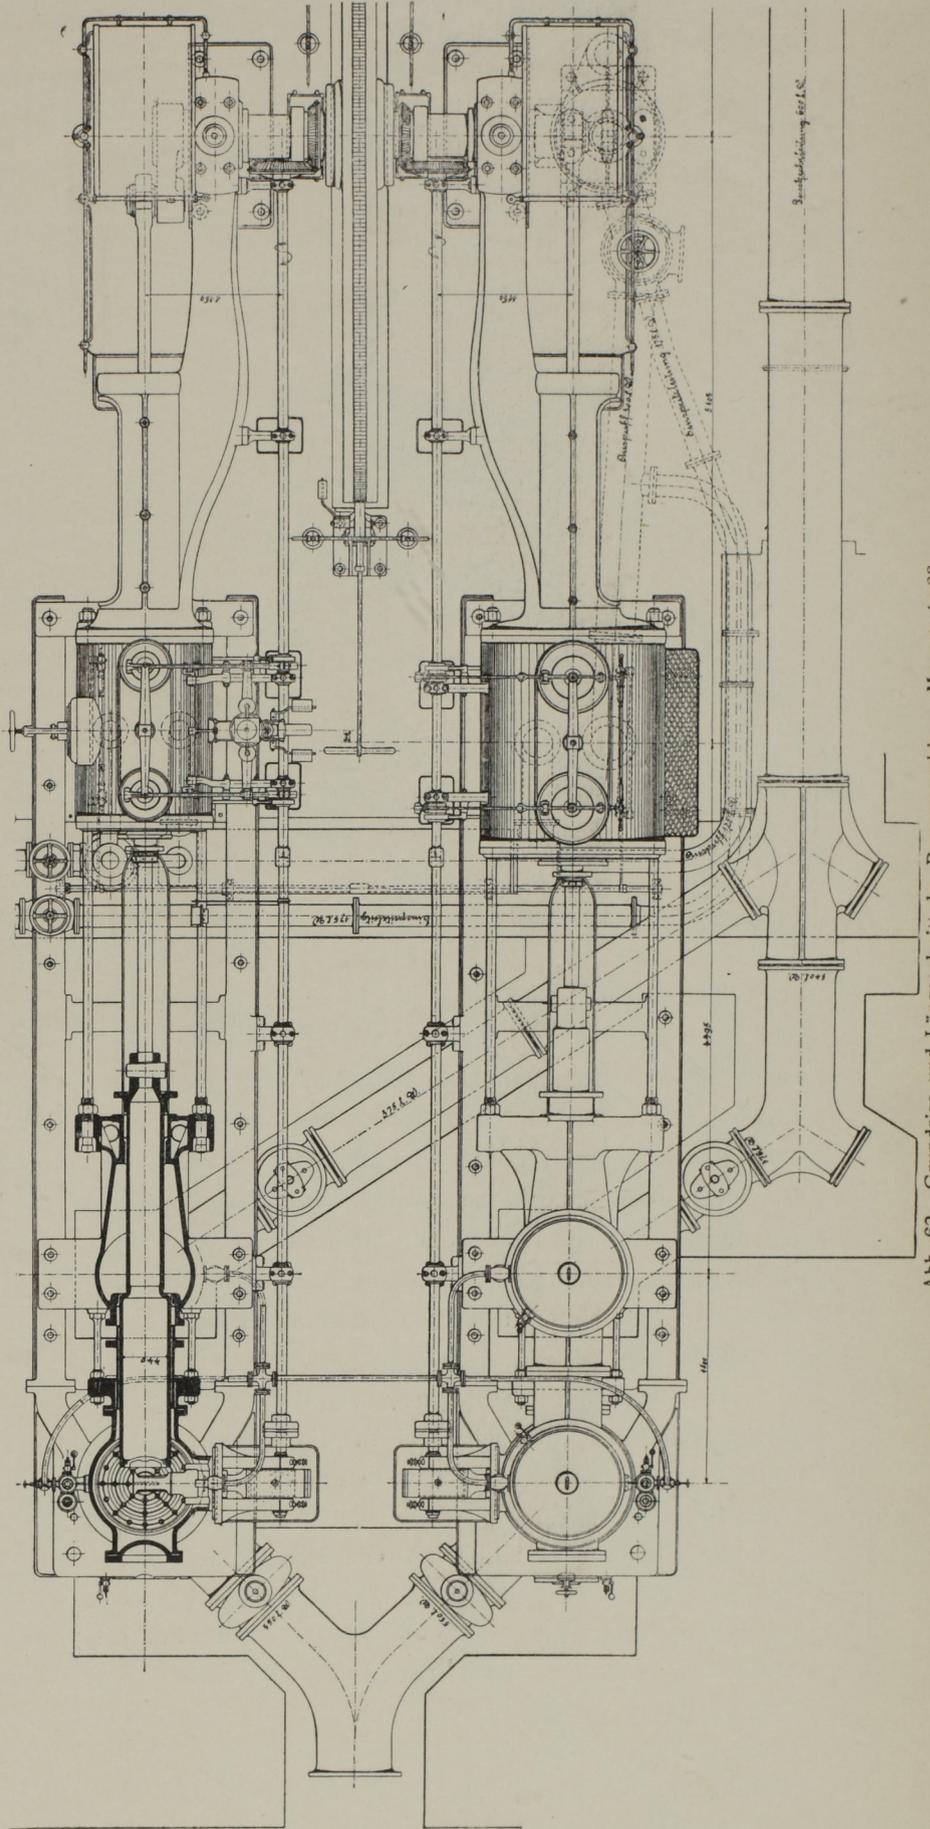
Grundriss und Längsschnitt der Pumpmaschine. Massst. 1:60.
